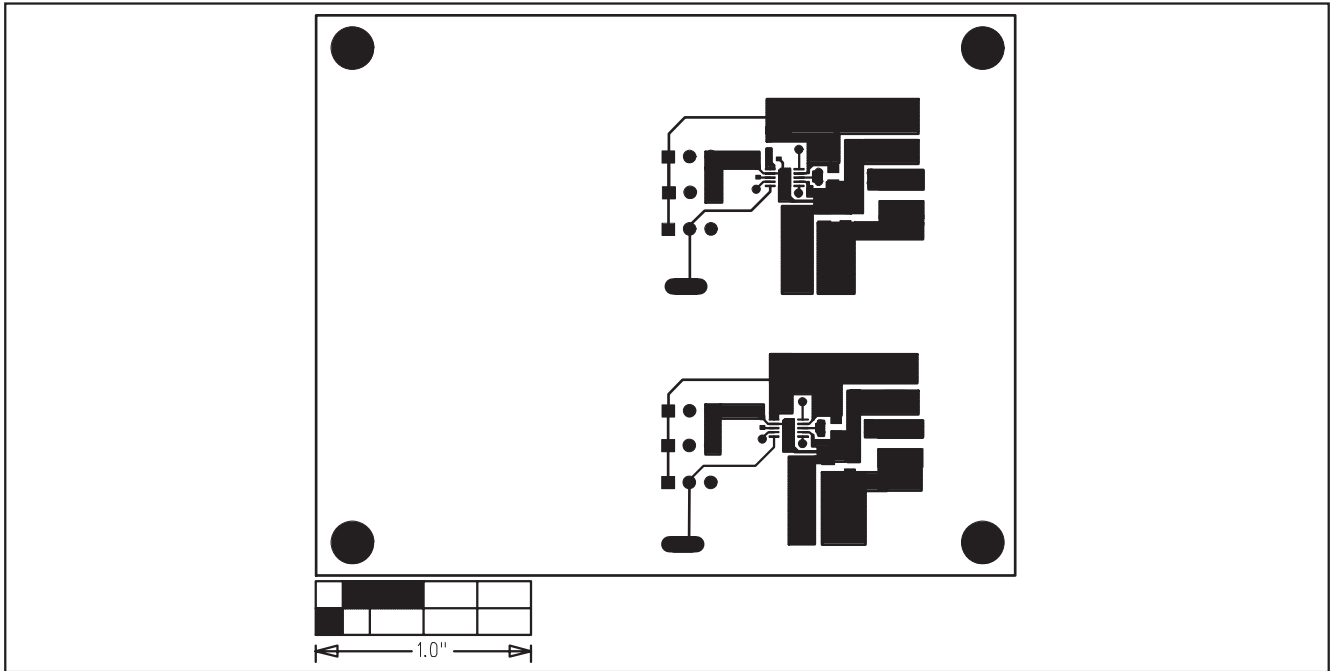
MAX1556 评估板 PCB 布局图 — 元件面
